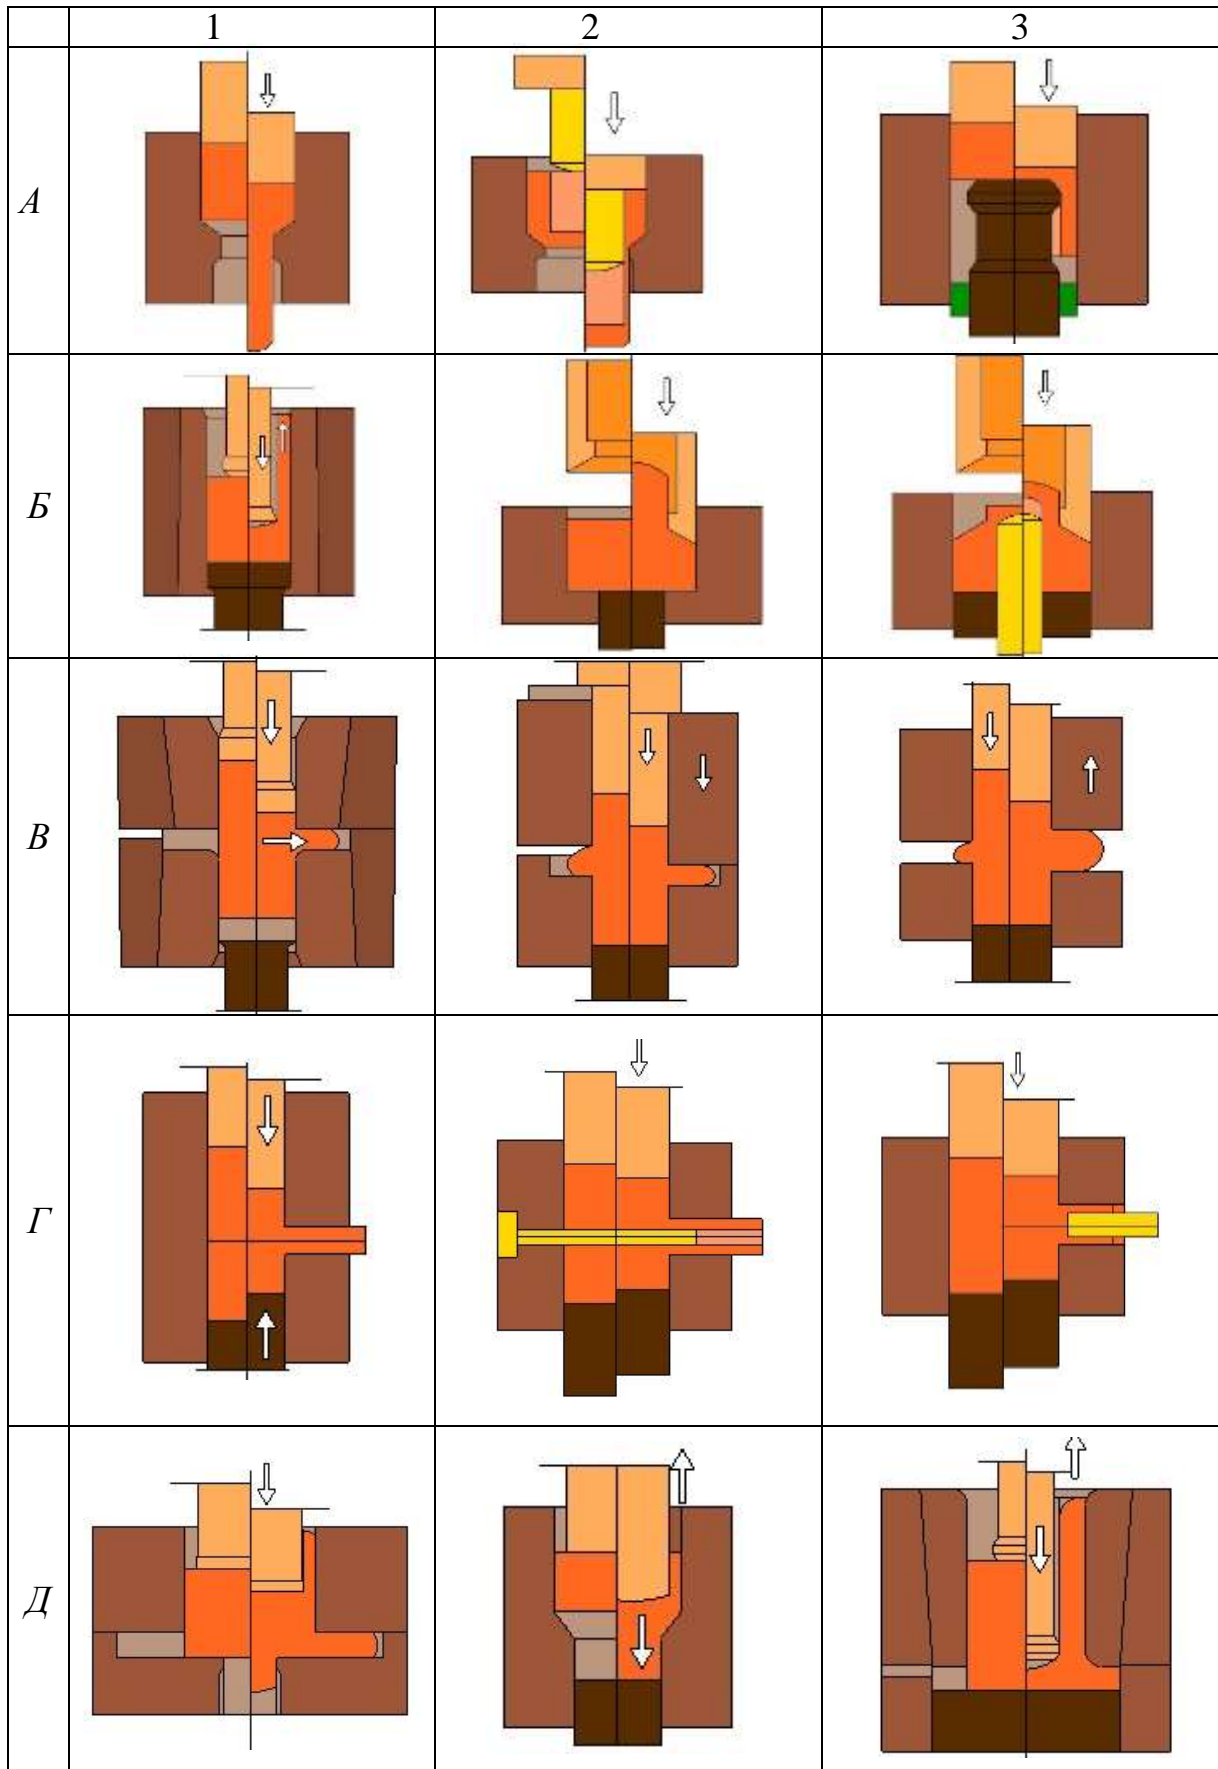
Застосування способів холодного видавлювання для виготовлення деталей різного типу
